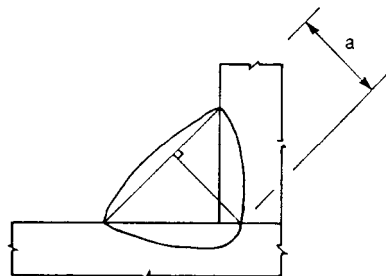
Espessura de um cordão de soldadura com elevada penetração
